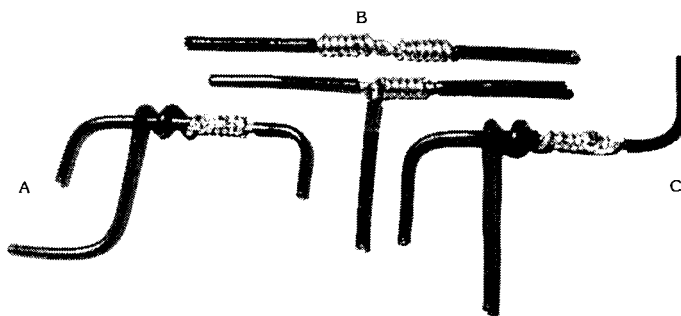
A - Soldagem feita com ferro a uma temperatura muito baixa. B - Soldagem feita após atingida a temperatura normal de funcionamento do ferro de solda. A soldagem é lisa e brilhante. C - Soldagem feita com excesso de solda.
